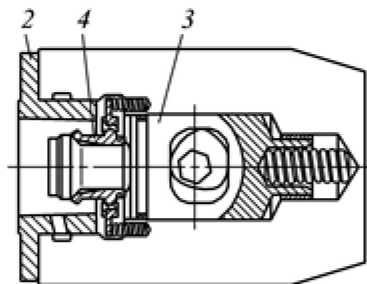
Устройство ручного закрепления хвостовиков Coromant Capto (обозначения — см. рис. 51)
